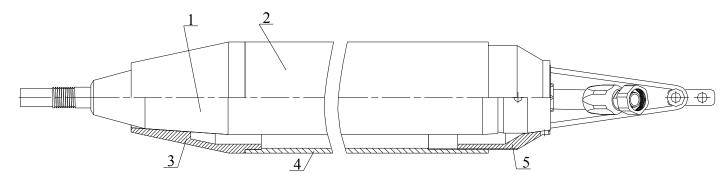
Схема установки расширителя реверсивного. 1 –пробойник ИП-4603A;
